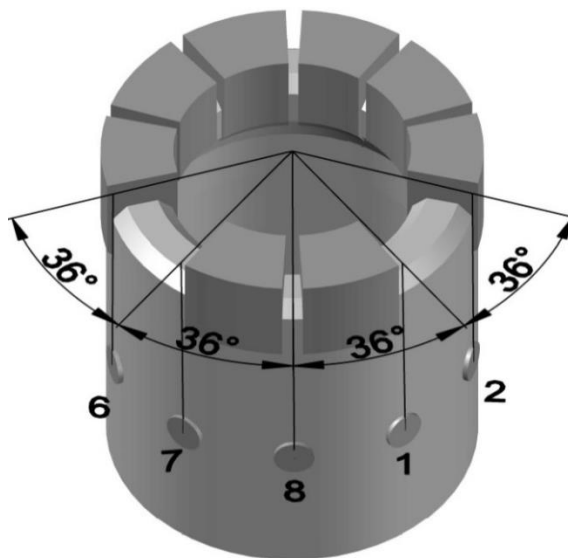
Схема расположения наплавов на корпусе опытной коронки КИТ: 1, 2, 6, 7, 8 – наплавки
